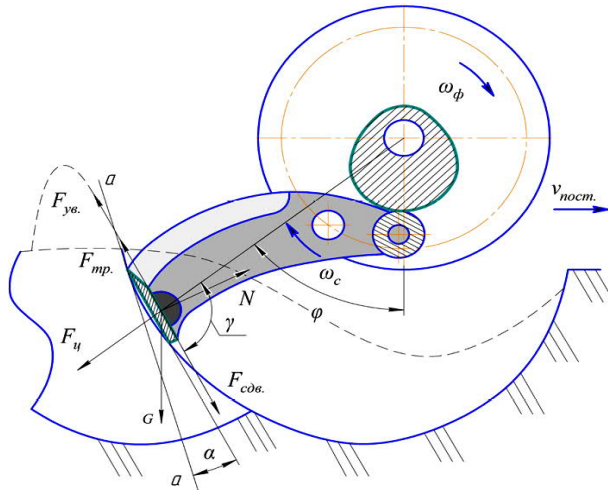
Адаптивная фреза с управляемыми углами резания ножей
